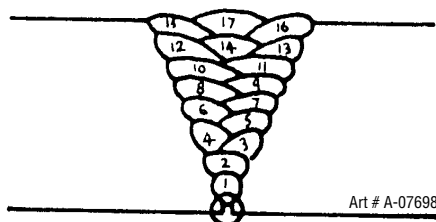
Séquence d'élaboration de la soudure
